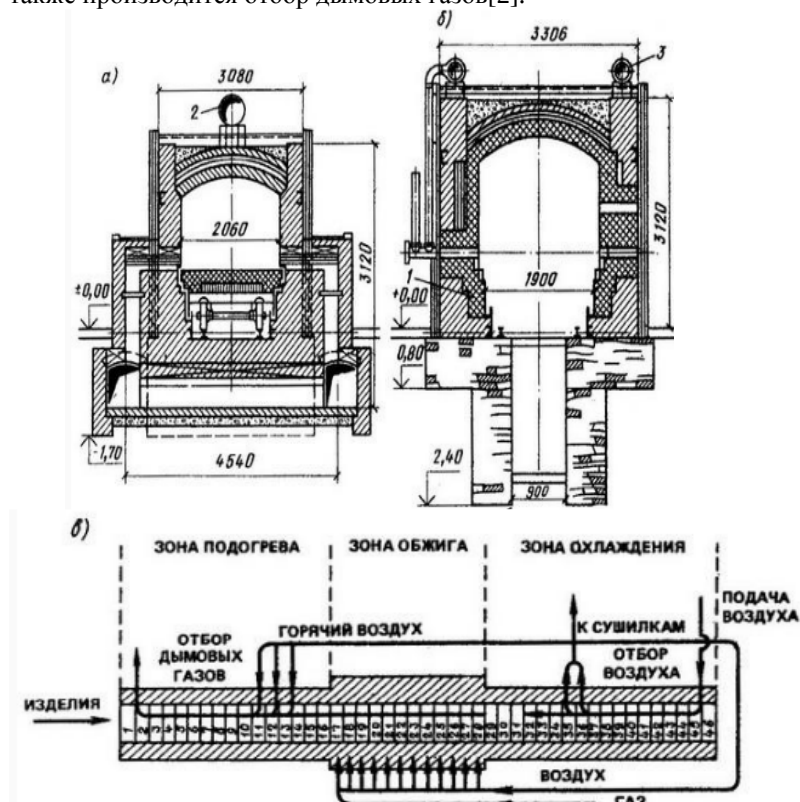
Современная туннельная печь для обжига кирпича: а — зона подогрева; б — зона взвара (1 — кладка печи; 2 — воздухопровод; 3 — газопровод); в — схема тепловых зон
